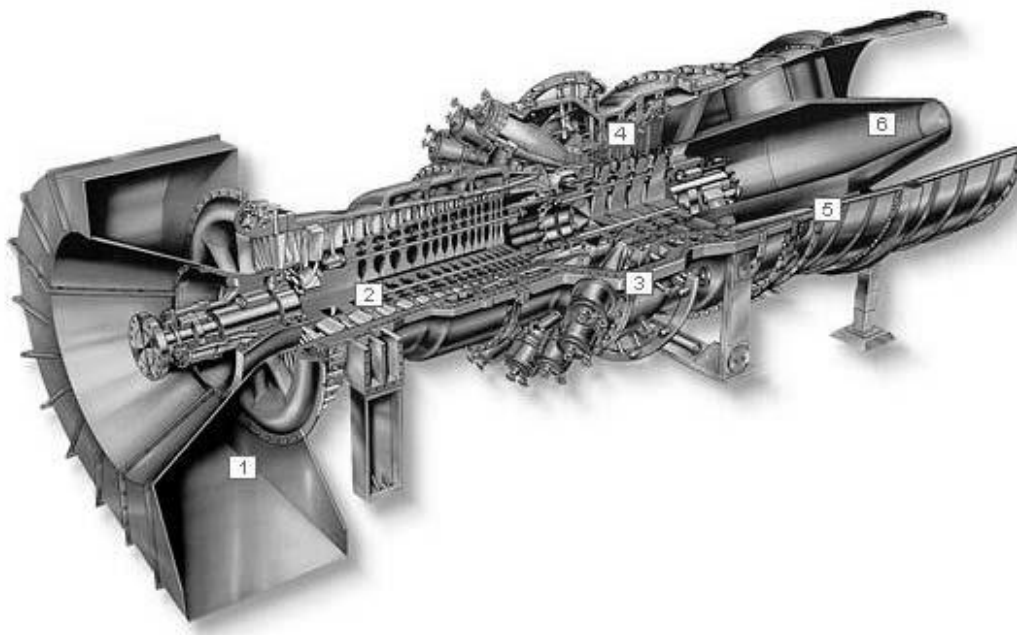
Turbina a gas Siemens-Westinghouse 501G [4]
